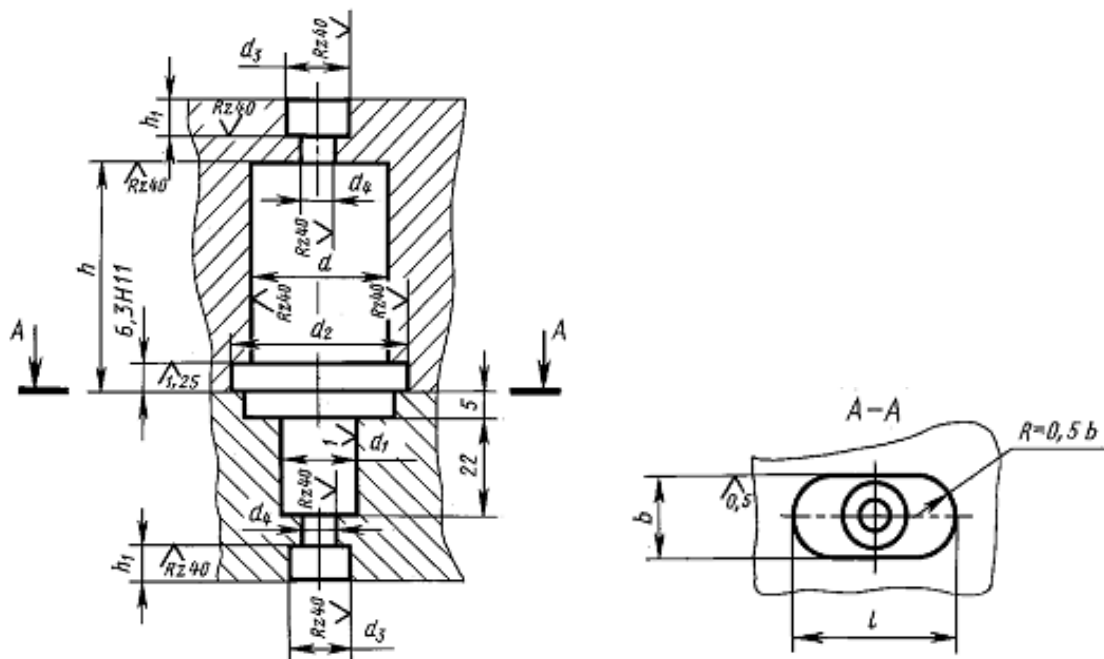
Конструкция гнезд для установки центрирующих соединений с винтовым креплением
